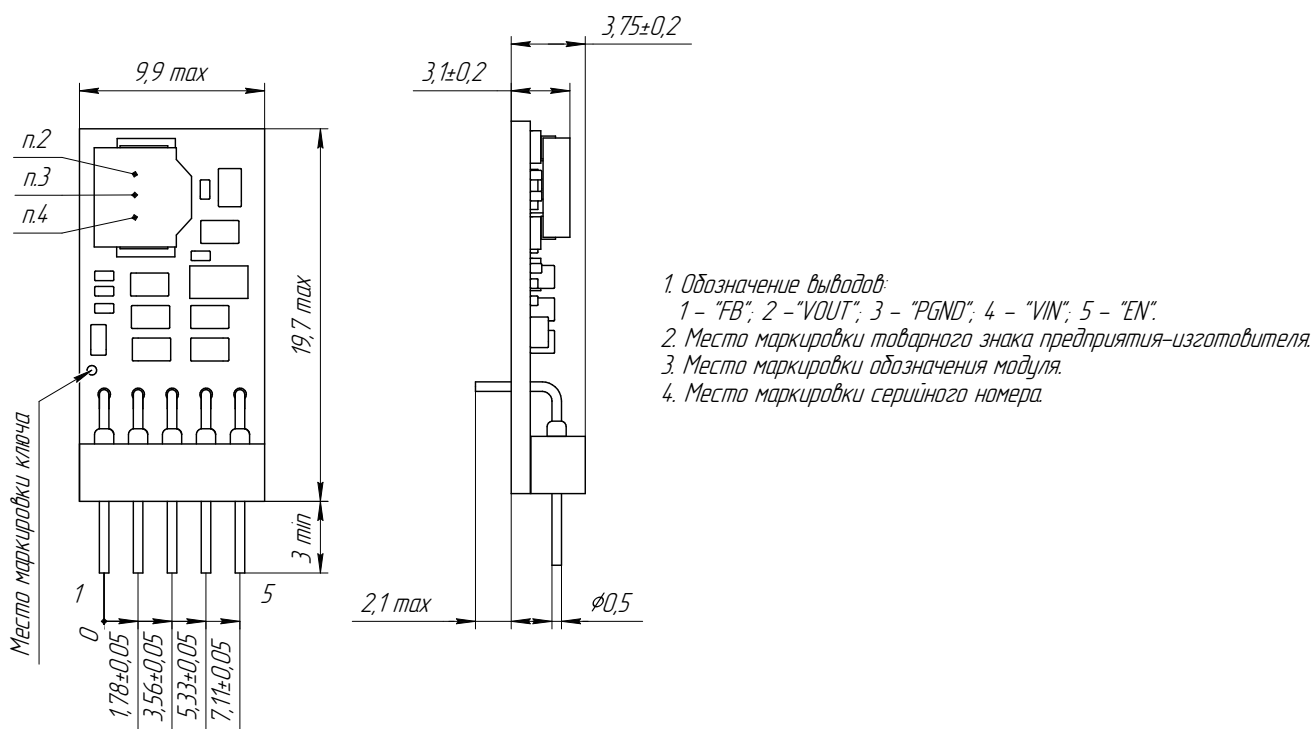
Габаритный чертеж и обозначение выводов VNA3LO, 87, OSP.
